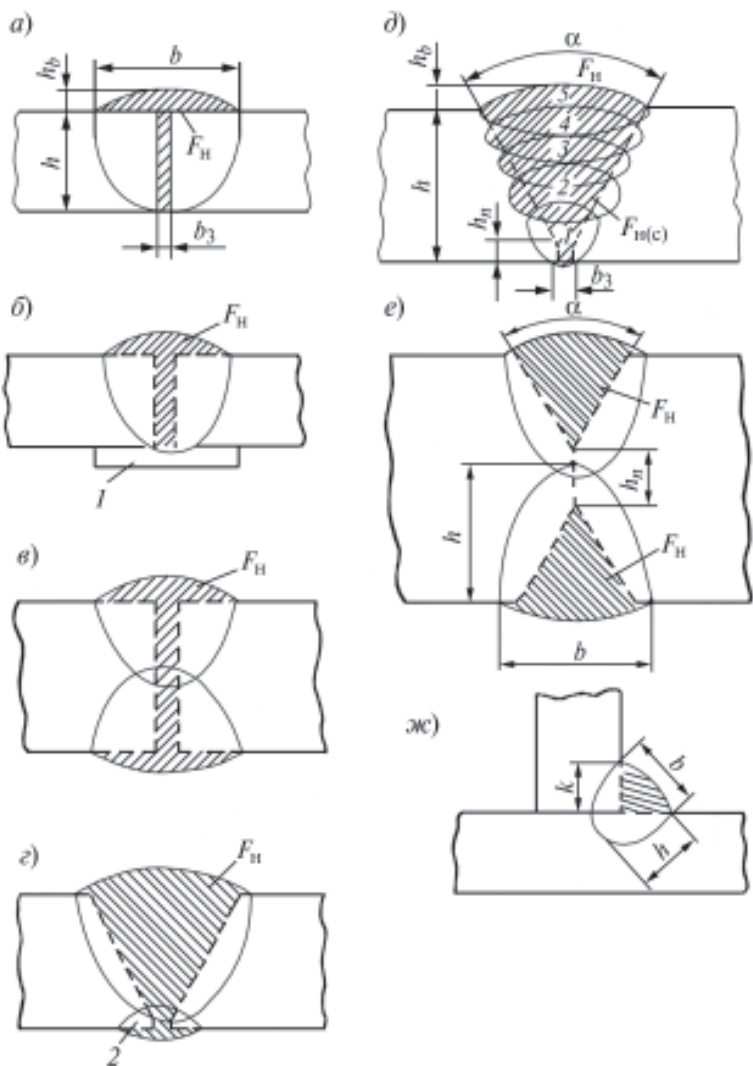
Размеры и формы подготовки кромок и сварного шва:
